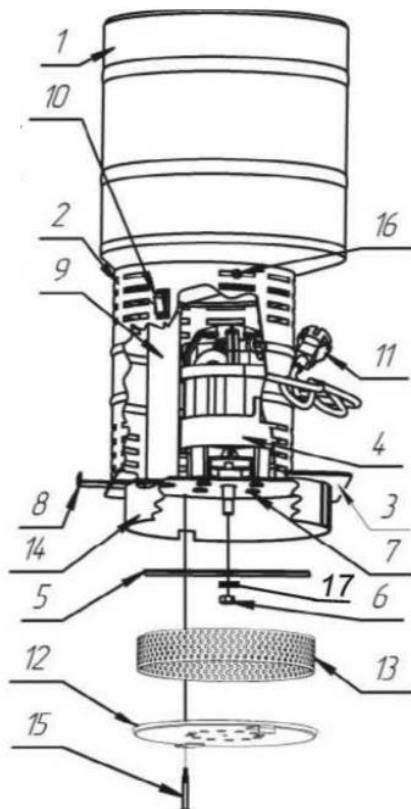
Устройство измельчителя зерна ИЗЭ-14 «Фермер»: 1 – бункер; 2 – кожух; 3 – основание; 4 – электродвигатель; 5 – нож; 6 – гайка; 7 – винт крепления электродвигателя; 8 – заслонка; 9 – приемная труба; 10 – выключатель; 11 – шнур питания; 12 – дно рабочей камеры; 13 – боковое сито; 14 – отражатель; 15 – винт крепления сита; 16 – винт крепления бункера; 17 – шайба пружинная
